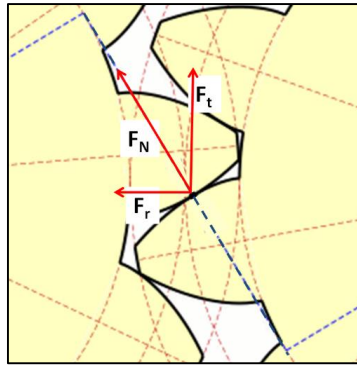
Fuerzas involucradas en el contacto entre dientes en un engranaje.
